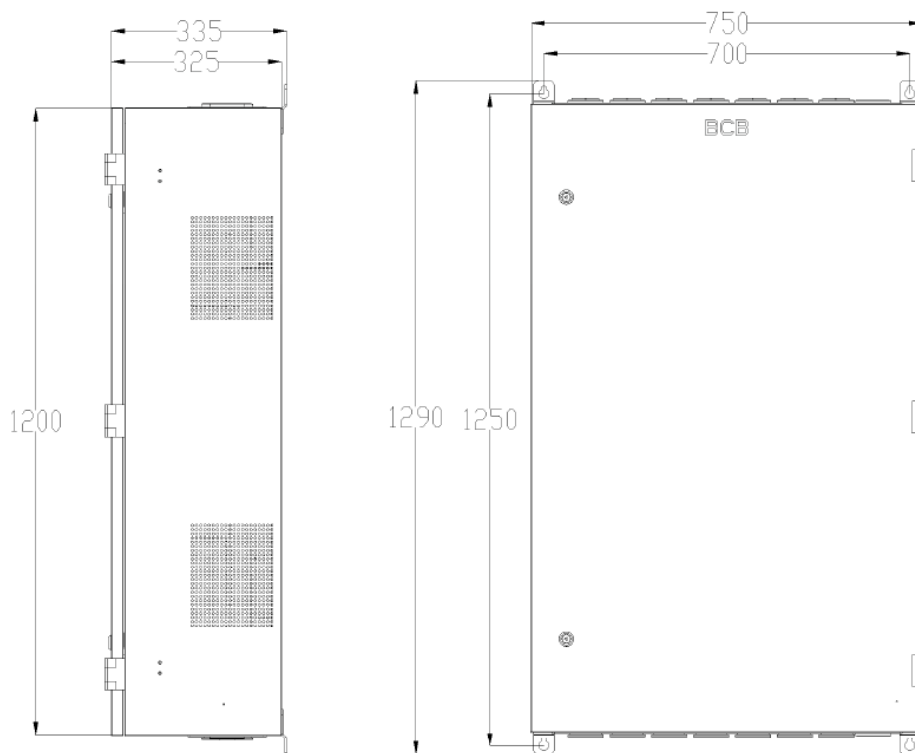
Размеры монтажных отверстий для настенного монтажа батарейного автомата ИБП 800 кВА (размеры в мм)
